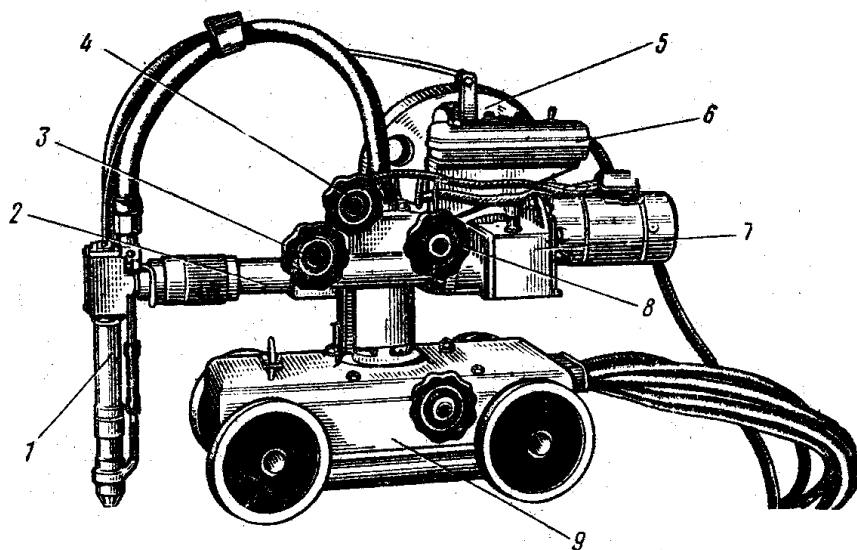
Сварочный трактор АДПГ-500:
